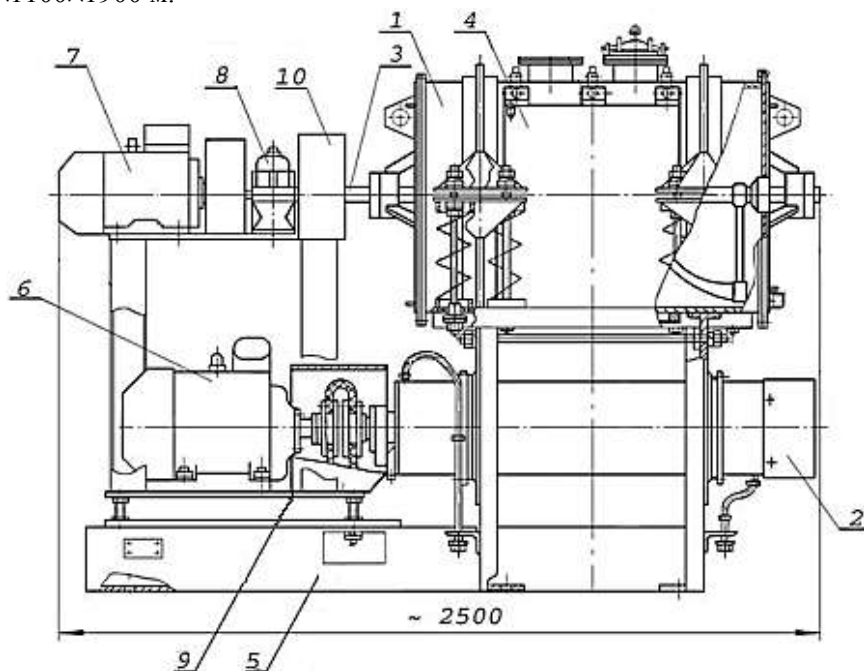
Смеситель СВП-0,3: 1 – камера; 2 – вибратор; 3 – вал мешалки; 4 – кожух; 5 – рама; 6 – двигатель вибратора; 7 – двигатель мешалки; 8 – редуктор; 9 – муфта вибратора; 10 – муфта мешалки.
